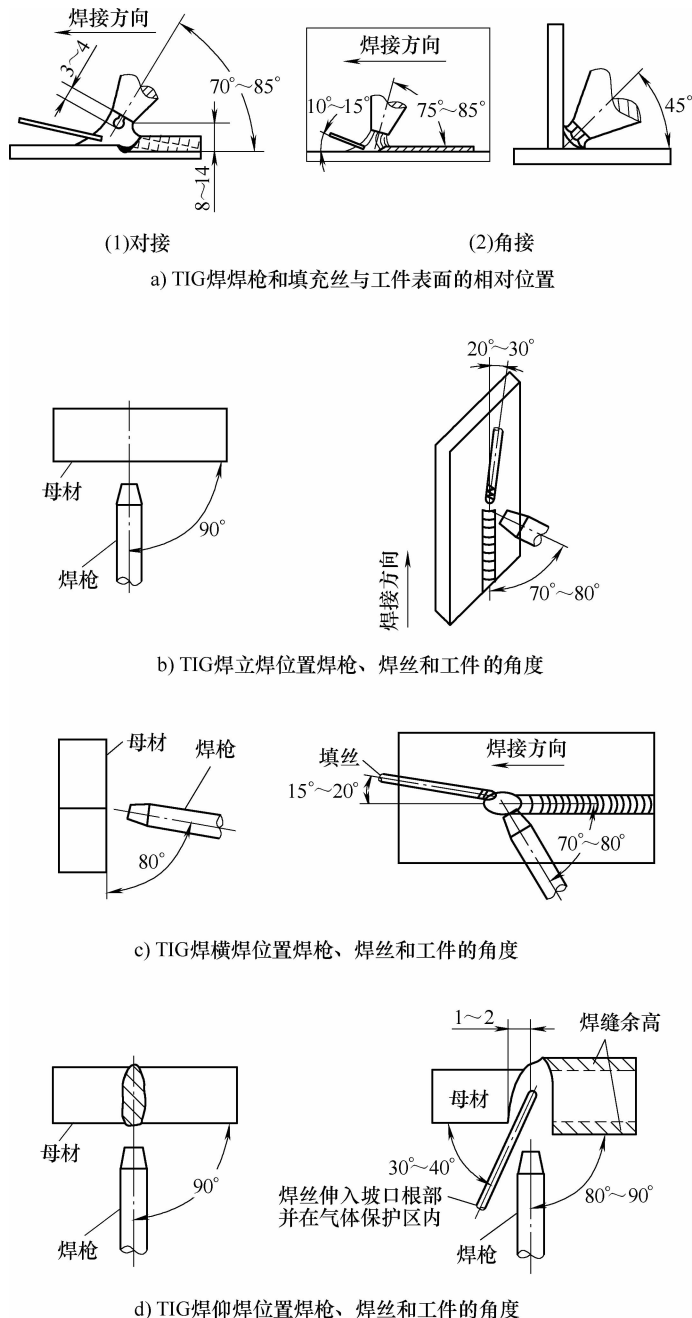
各种位置焊枪焊丝和工件的相对位置图
